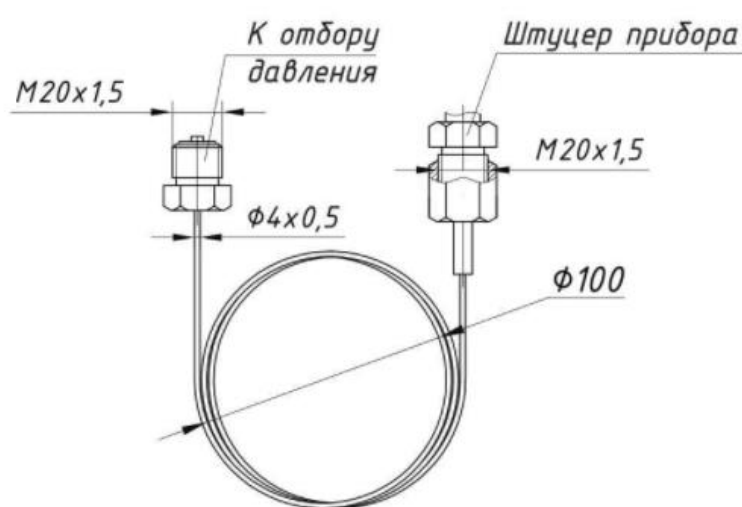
Габаритные и присоединительные размеры Рукав соединительный
